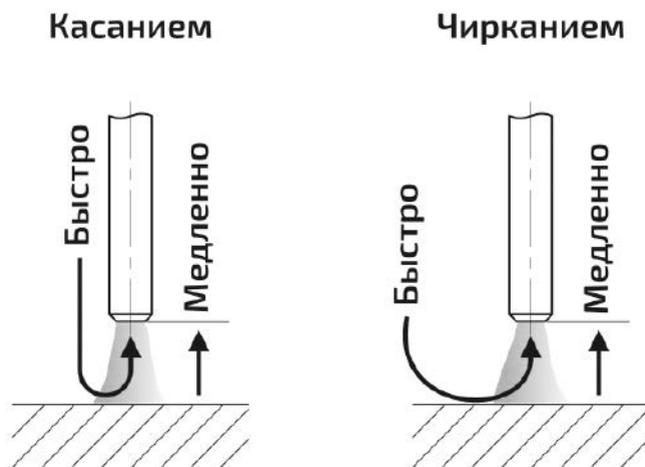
Способы зажигания сварочной дуги.
